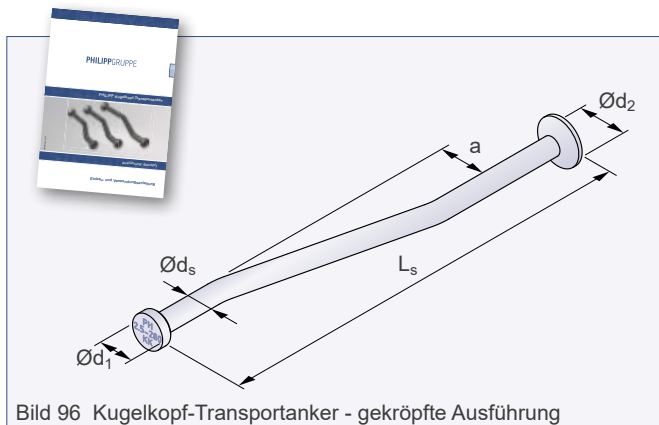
Kugelkopf-Transportanker - gekröpfte Ausführung
